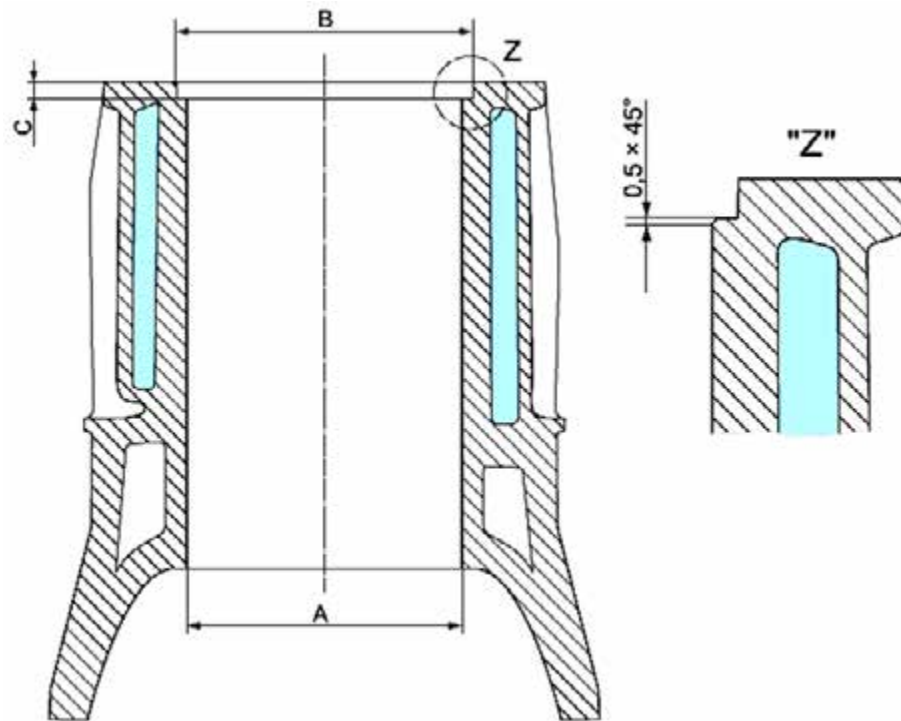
ro-47: Основные размеры отверстия в блоке цилиндров под за-
